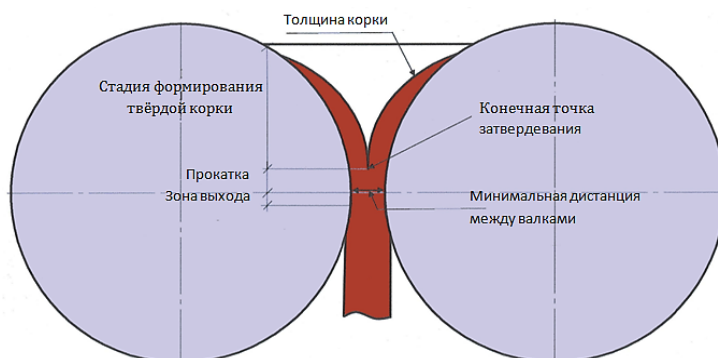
Схема двухвалковой разливки-прокатки, подчеркивающая аспекты ванны жидкого расплава и образования твердой корки
